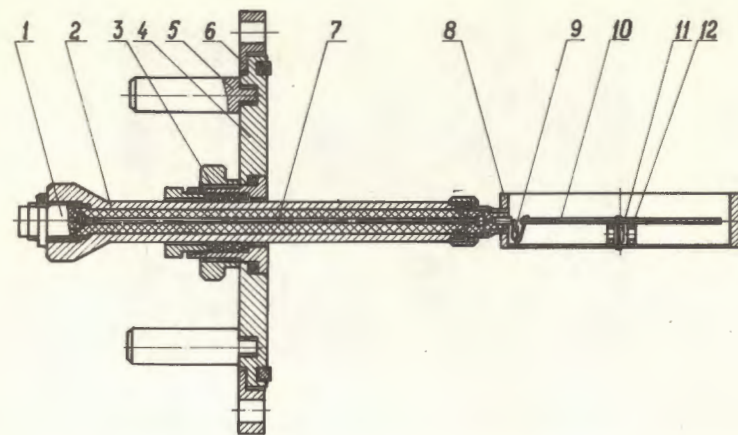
Цилиндр Фарадея. 1 - вакуумный разъем, 2 - шток, 3 - вакуумный узел, 4 - фланец, 5 - ручки для обеспечения регулировок, 6 - накидной фланец, 7 - внутренняя жила коаксиального фидера, 8 - корпус цилиндра, 9,11 - сопротивления делителя, 10 - медная пластина, 12 - фторопластовая шайба.
